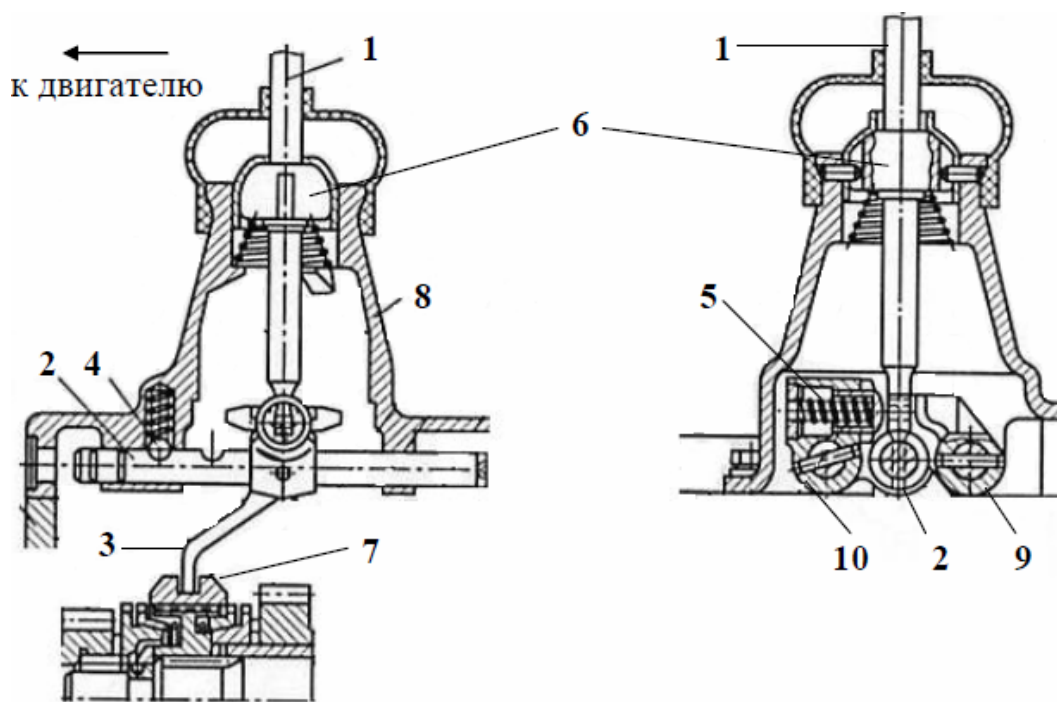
Детали механизма управления вальной коробкой передач:
